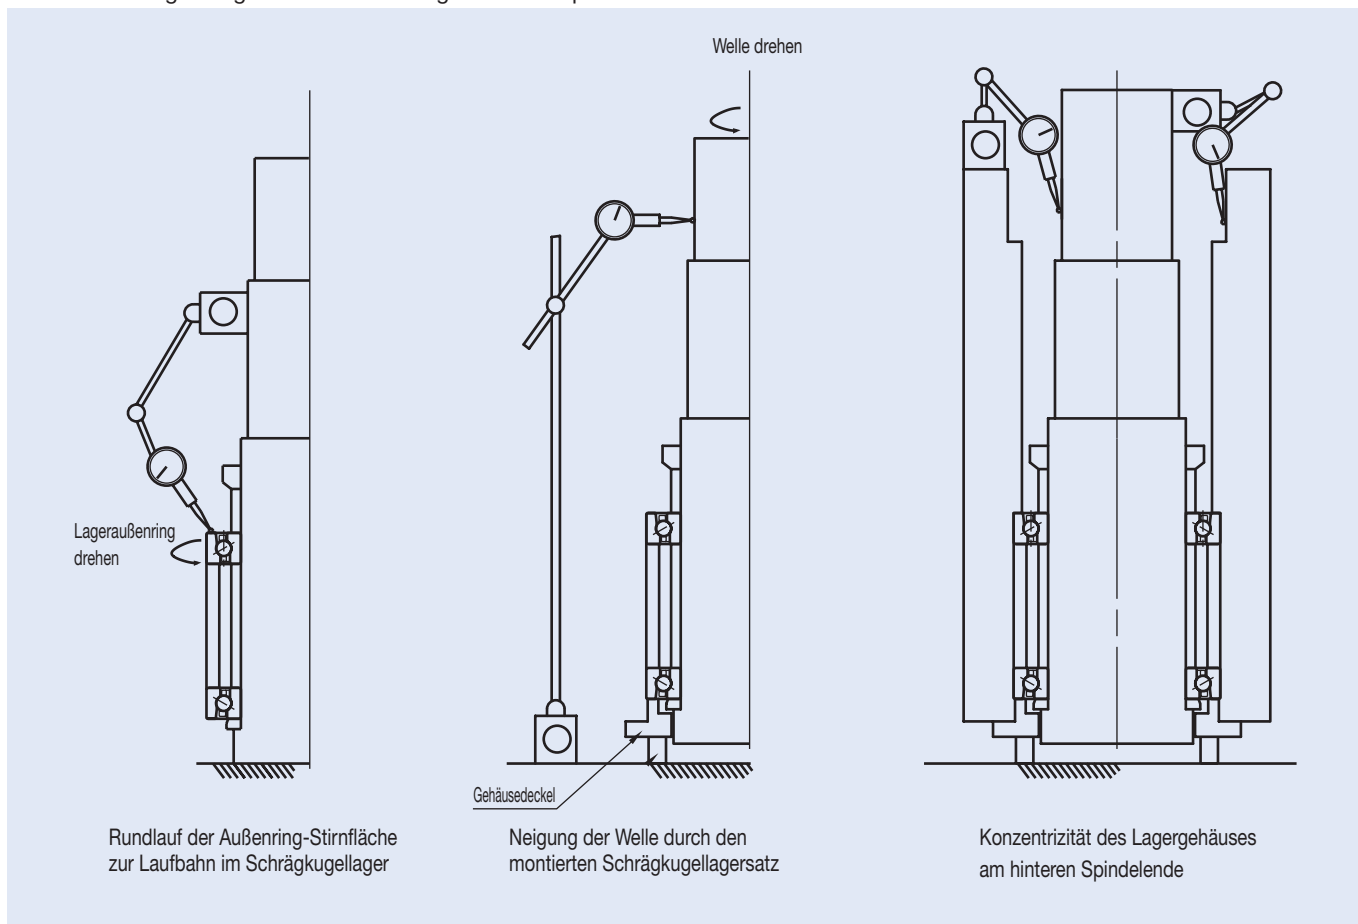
Laufgenauigkeit einer Werkzeugmaschinenspindel
